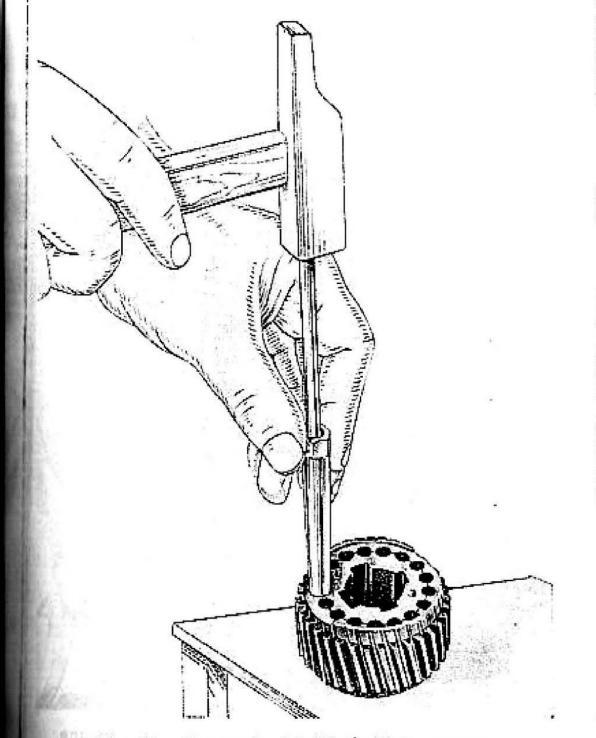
Montaggio del cilindretti in gomma nel pignone elastico motore.
